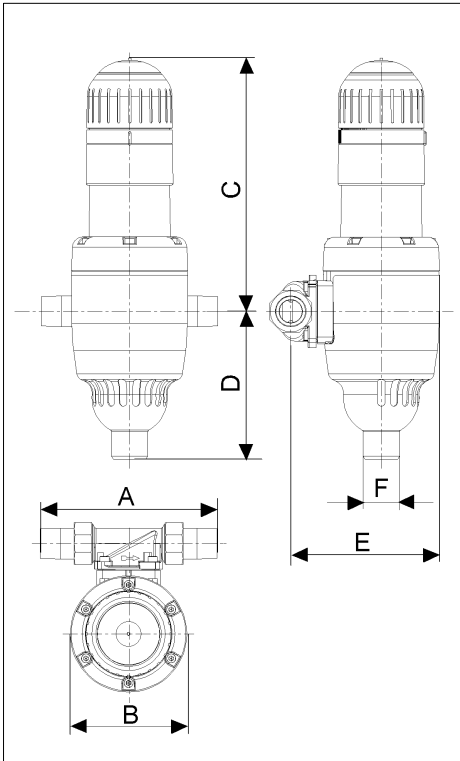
Installed dimensions  $\frac{3}{4}$ " - 1"
